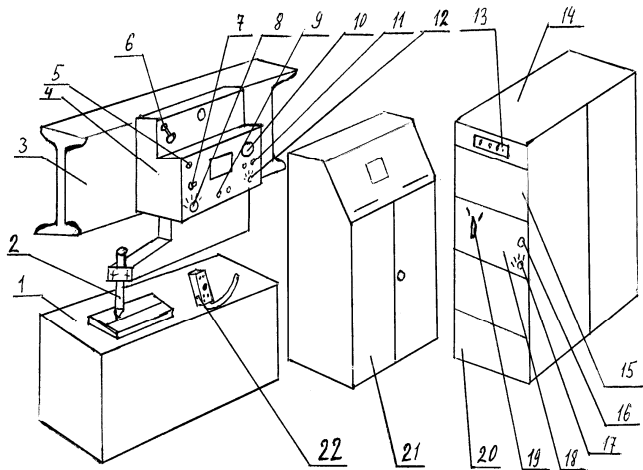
Компоновочная схема сварочного поста
